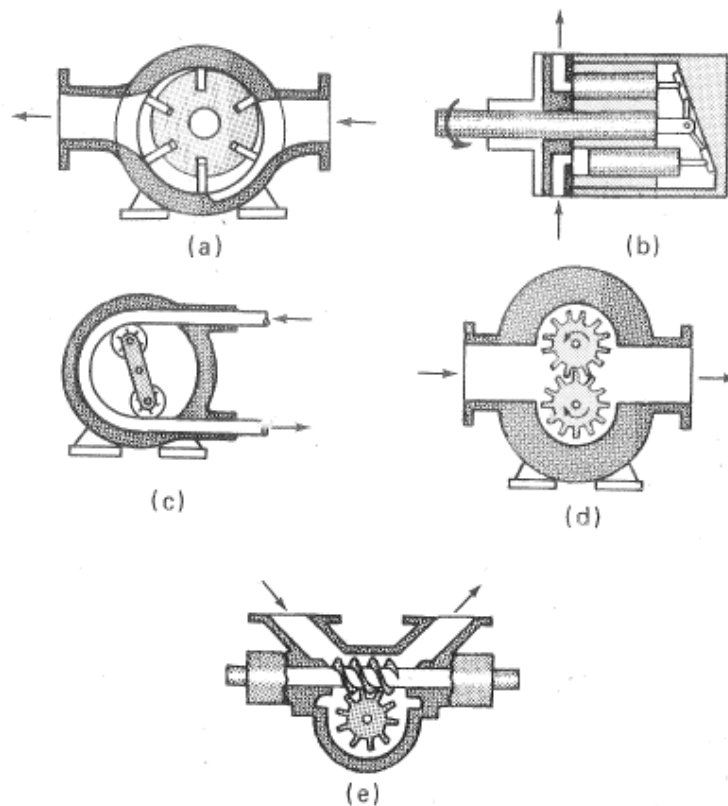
Bombas de desplazamiento positivo. a) B de paletas deslizantes; b) B de émbolos axiales; c) B de tubo flexible; d) B de engranajes exteriores; e) B de engranaje y tornillo.
